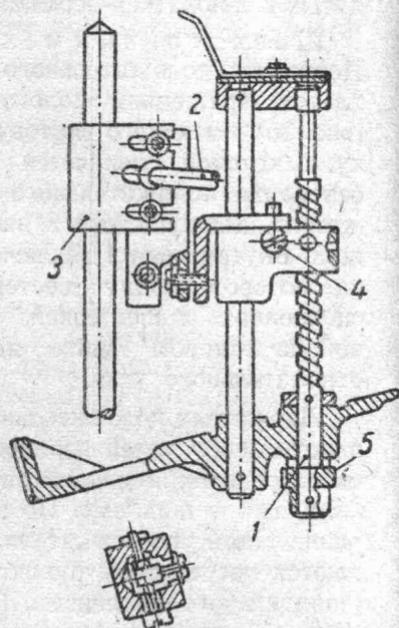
Держатель отрицательного угля: 1 — ходовой винт; 2 — рукоятка зажима угля; 3 — переставной угольник; 4 — винт перемещения угля; 5 — шестеренка
